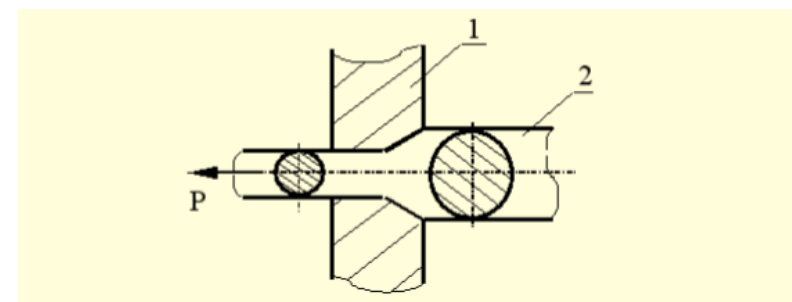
Схема процесса волочения: 1 – матрица, 2 – заготовка
